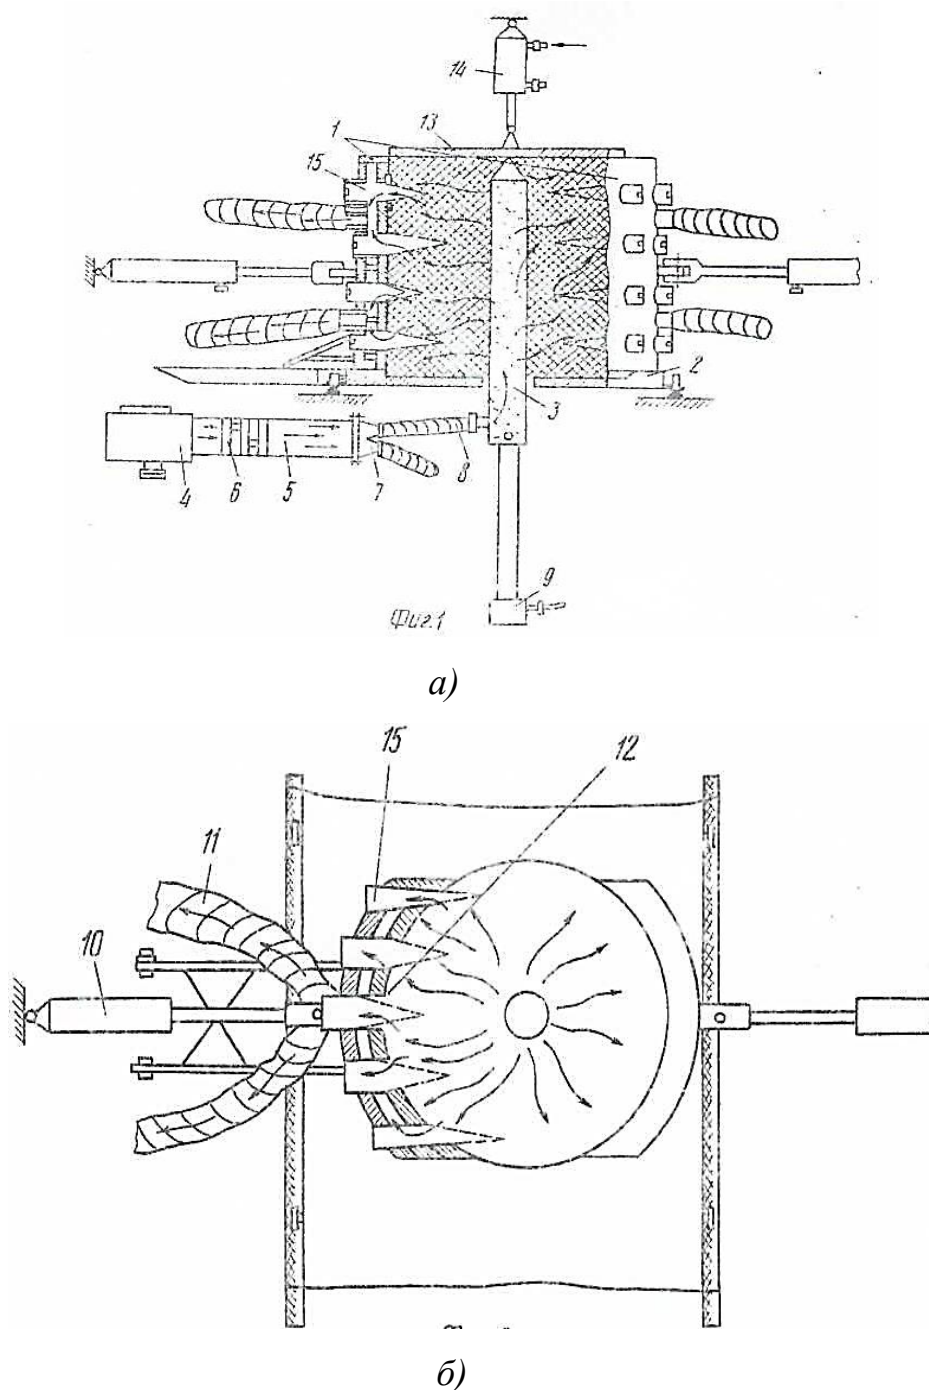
Сушарка рулонів: а – вид збоку; б – вид зверху [10]
